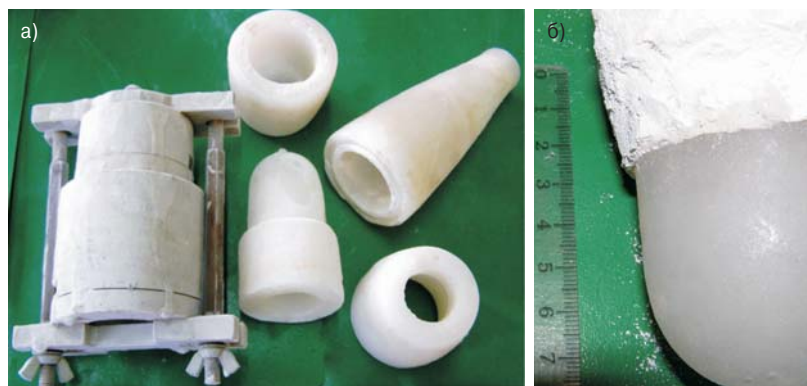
Ледяная модель для изготовления колпачка (а) с нанесенной ПК (б)
